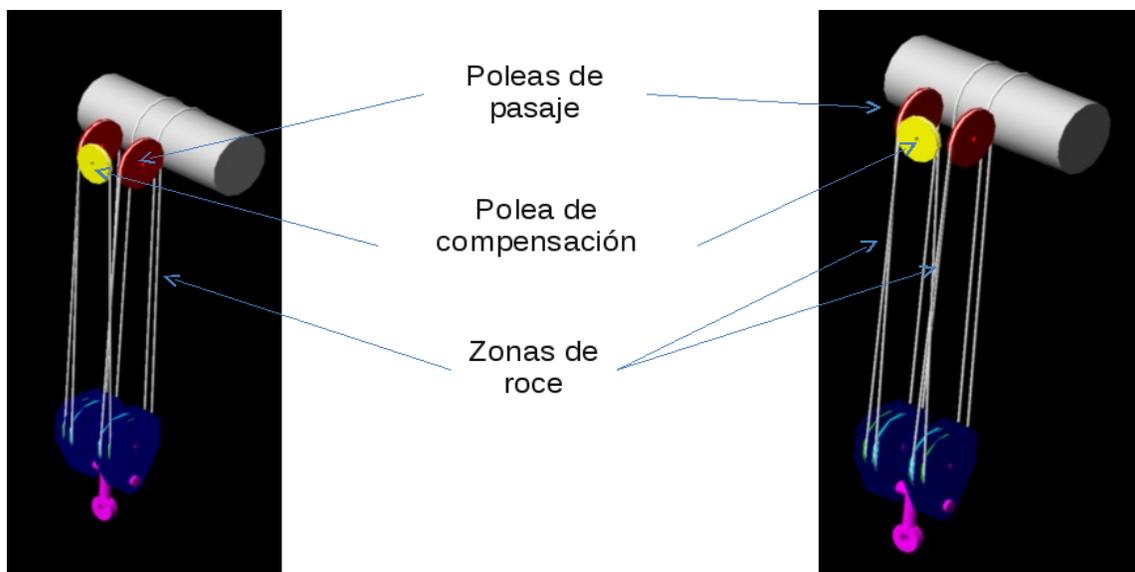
Esquema de pasaje de los cables (rope reeving) de un gancho de la grúa 3x140 t. Las zonas de roce entre las guayas son mostradas
